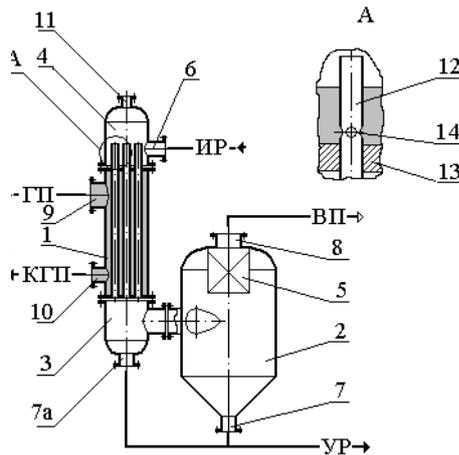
Вертикальный трубчатый выпарной аппарат со стекающей пленкой раствора
